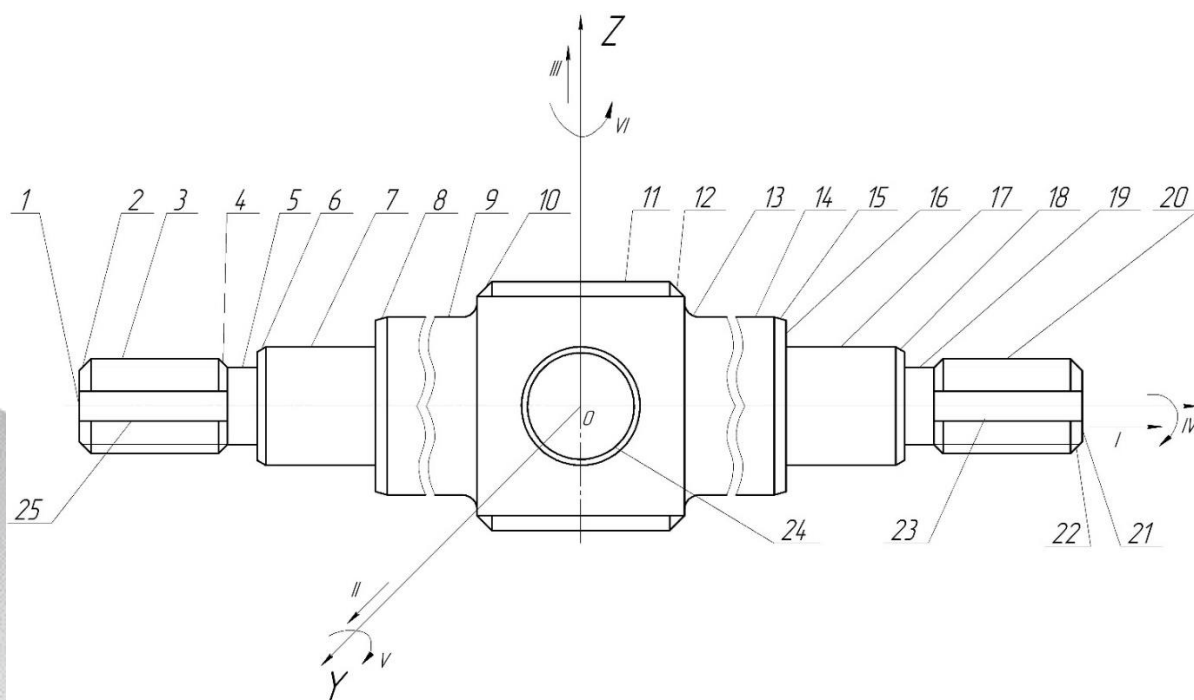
Вал проміжний з пронумерованими поверхнями деталі
